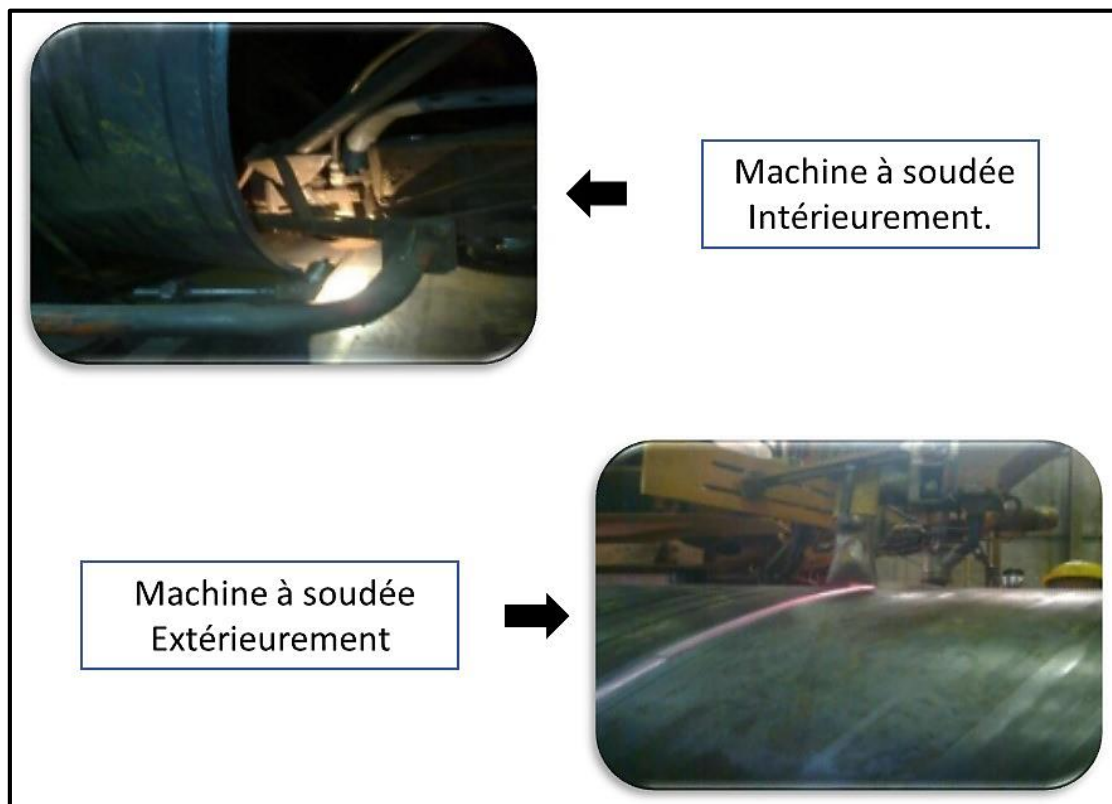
Tube préparé à la machine soudée en spirale
